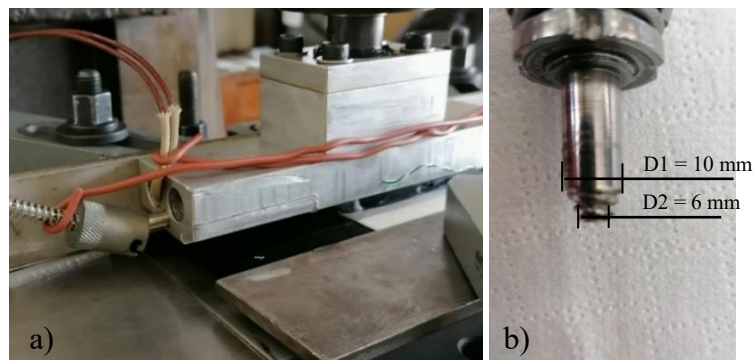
Ferramenta de soldadura de polímeros por FSW.
